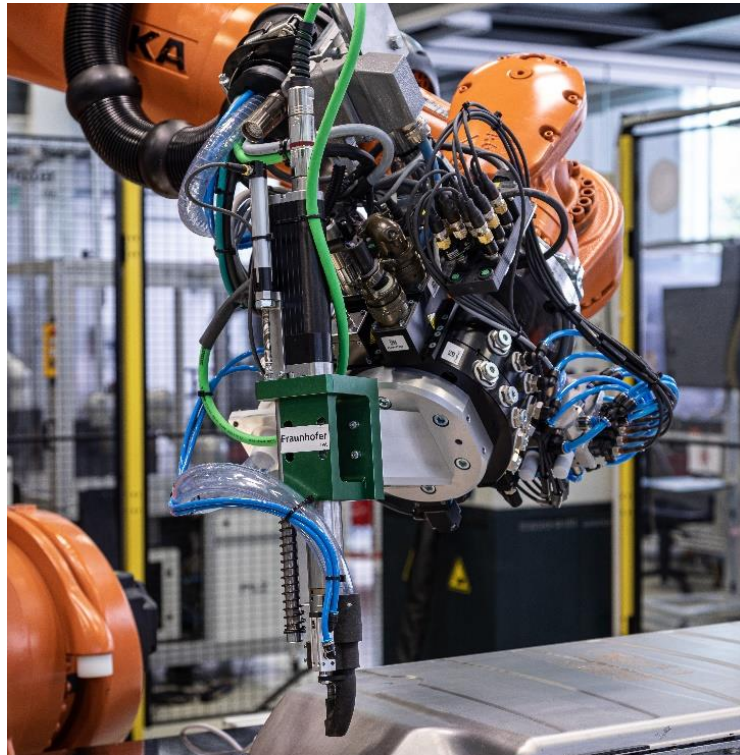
Werkzeug zum Lösen und Abführen der Schrauben.
